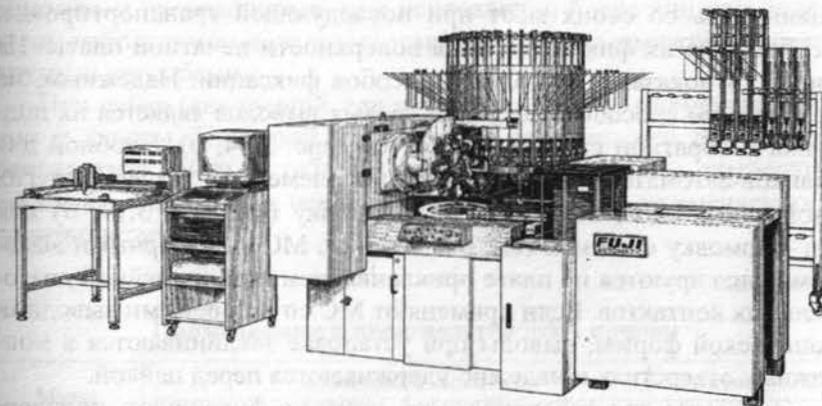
Общий вид станка-автомата фирмы Fuji для установки на плату элементов с осевыми выводами
